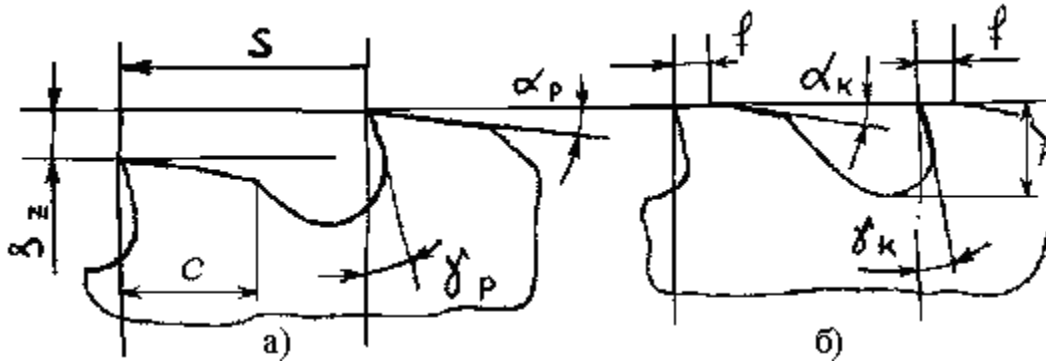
Профиль: а) режущих и б) калибрующих зубьев протяжки
